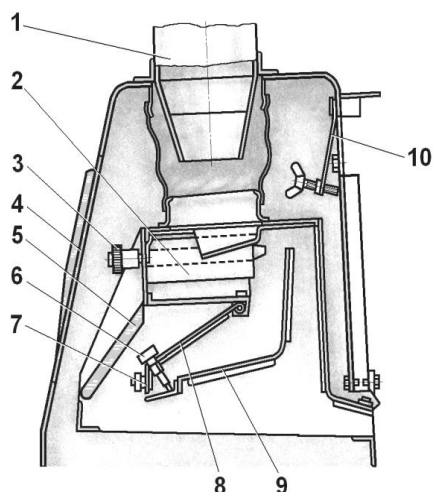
Схема живильника-розподільника: 1 – патрубок живильний; 2 – коробка приймальна; 3 – ручка; 4 – дверка; 5 – кришка; 6 – гвинт регулювальний; 7 – планка; 8 – клапан розподільний; 9 – скат; 10 – клапан аспіраційний
